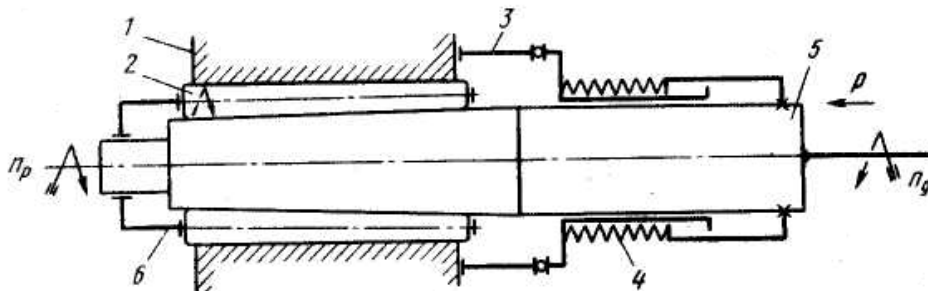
Кінематична схема роlikової частини інструменту для обробки переривчастих отворів: 1 – деталь; 2 – ролик; 3 – опорна втулка; 4 – пружина; 5 – конусна оправка; 6 – сепаратор.
